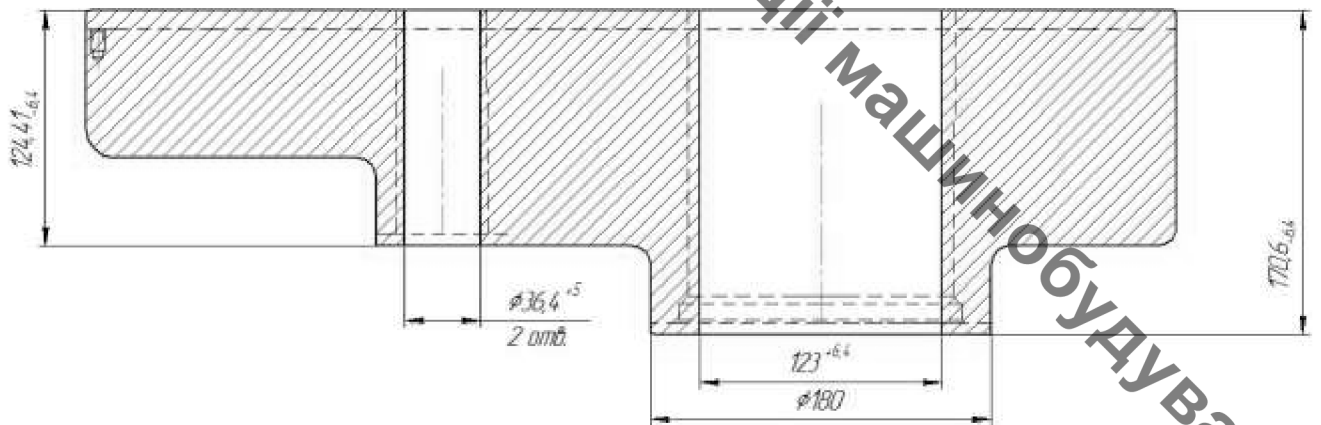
Ескіз заготовки в піщано-глинисті форми
